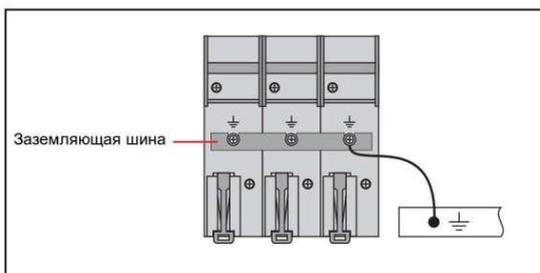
Заземляющая шина. Внешний вид, монтаж.
